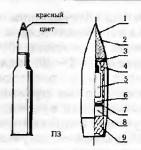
Пристрелочно-зажигательная пуля ПЗ: 1 — оболочка; 2 — зажигательный состав; 3 — рубашка взрывателя; 4 — капсуль-воспламенитель; 5 — предохранитель; 6 — ударник; 7 — стаканчик: 8 — прокладка малая; 9 — прокладка большая
